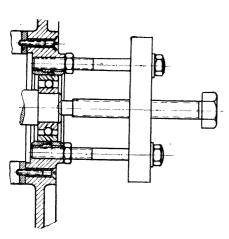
Снятие подшипникового щита со стороны контактных колец
